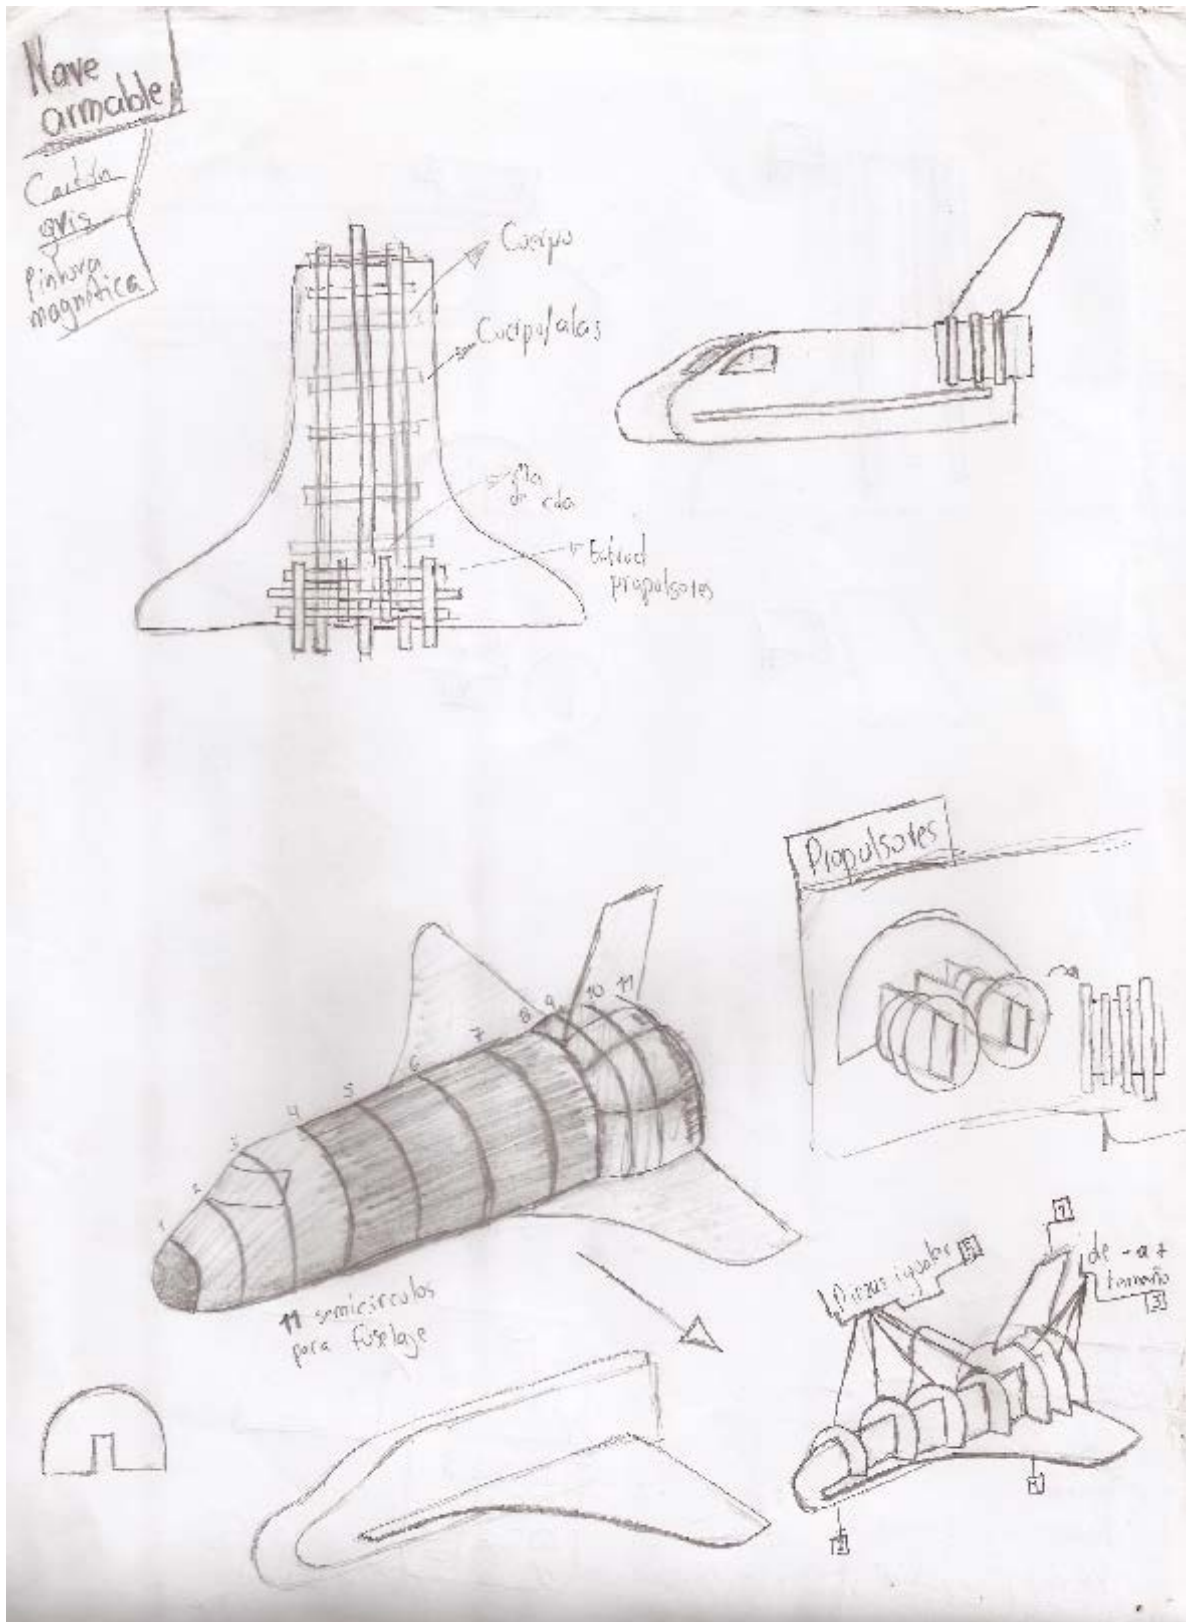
Despiece de la nave armable para definir piezas y sistemas de encaje.
